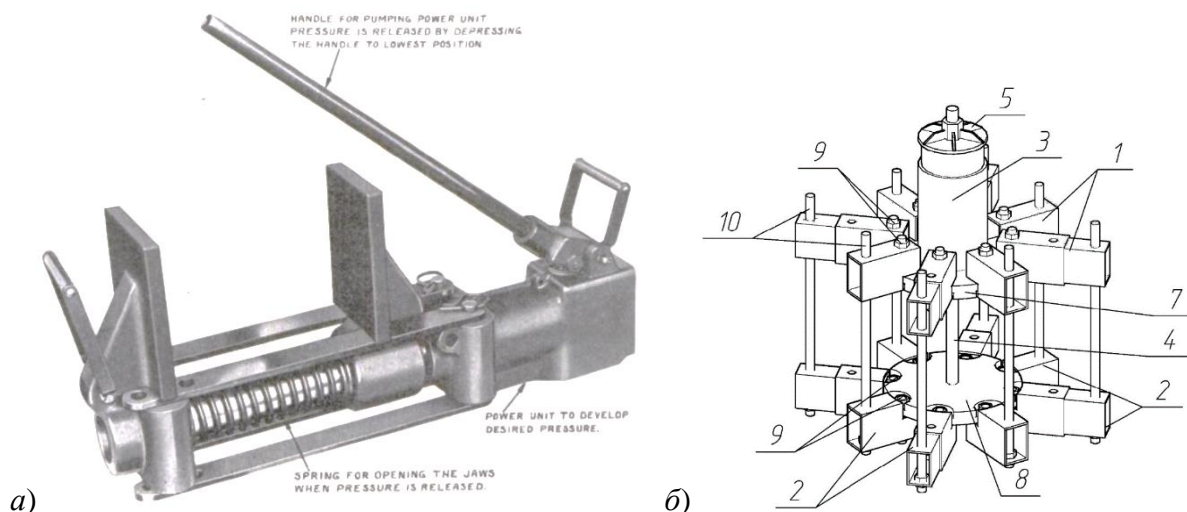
Устройство для запрессовки когтевых шайб: а) модифицированный пресс производства Greenlee Bros. & Co (США) [4]; б) гидравлический пресс с кондуктором для запрессовки когтевых шайб [8].
